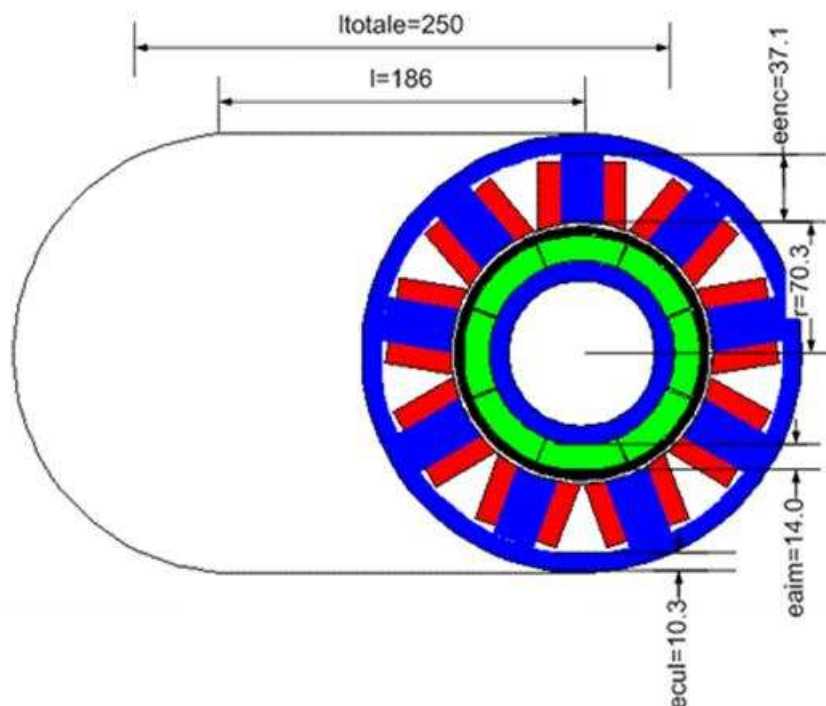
Aspect et dimensions de la machine 8-9 en (mm)
